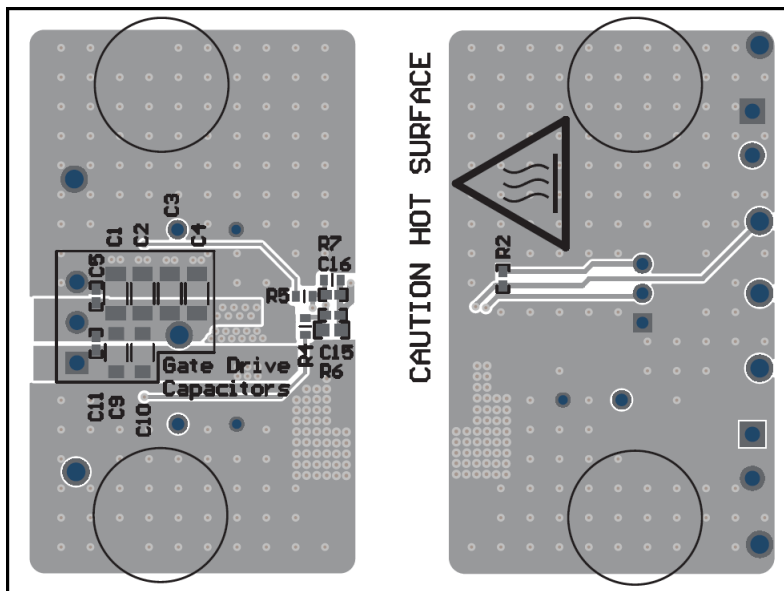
UCC14141-Q1EVM, PCB Bottom Layer, Assembly (Mirrored View)
